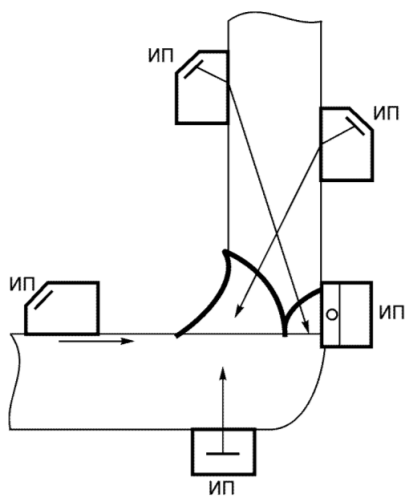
Схема прозвучивания углового сварного соединения при двустороннем доступе совмещенными наклонными и прямым преобразователями, преобразователями подповерхностных (головных) волн
